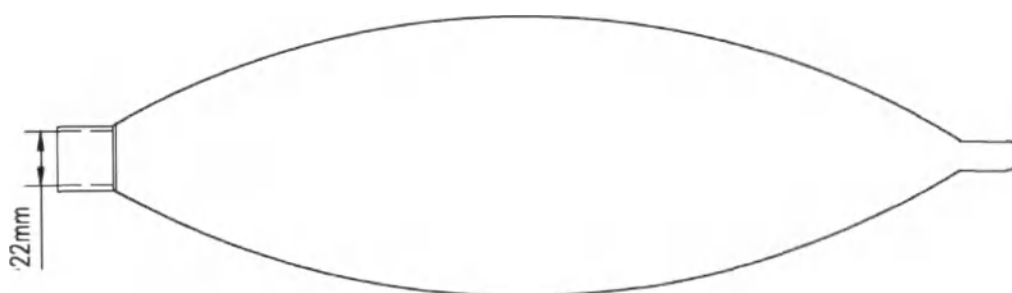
Мешок резервуарный для дыхательного контура
